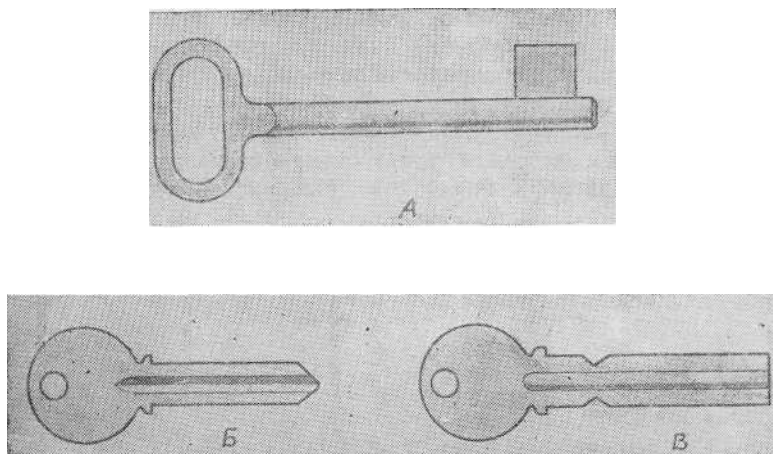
Болванки для изготовления ключей: А — для сувальдного и пружинного замка Б — для цилиндрического замка со штифтами в цилиндре В — для цилиндрического замка с пластинками в цилиндре
